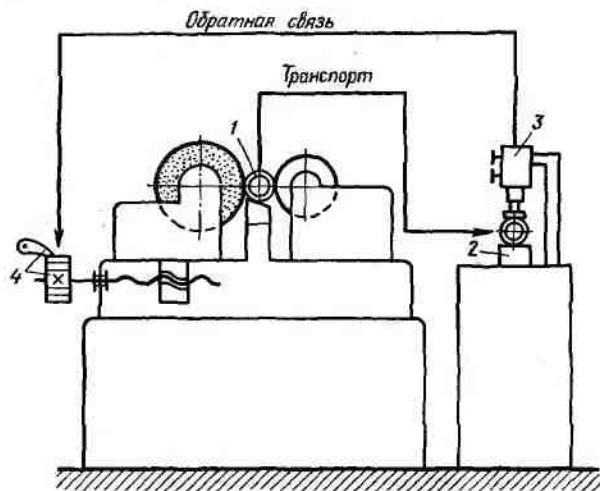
Схема подналадочной системы для бесцентровошлифовального станка
